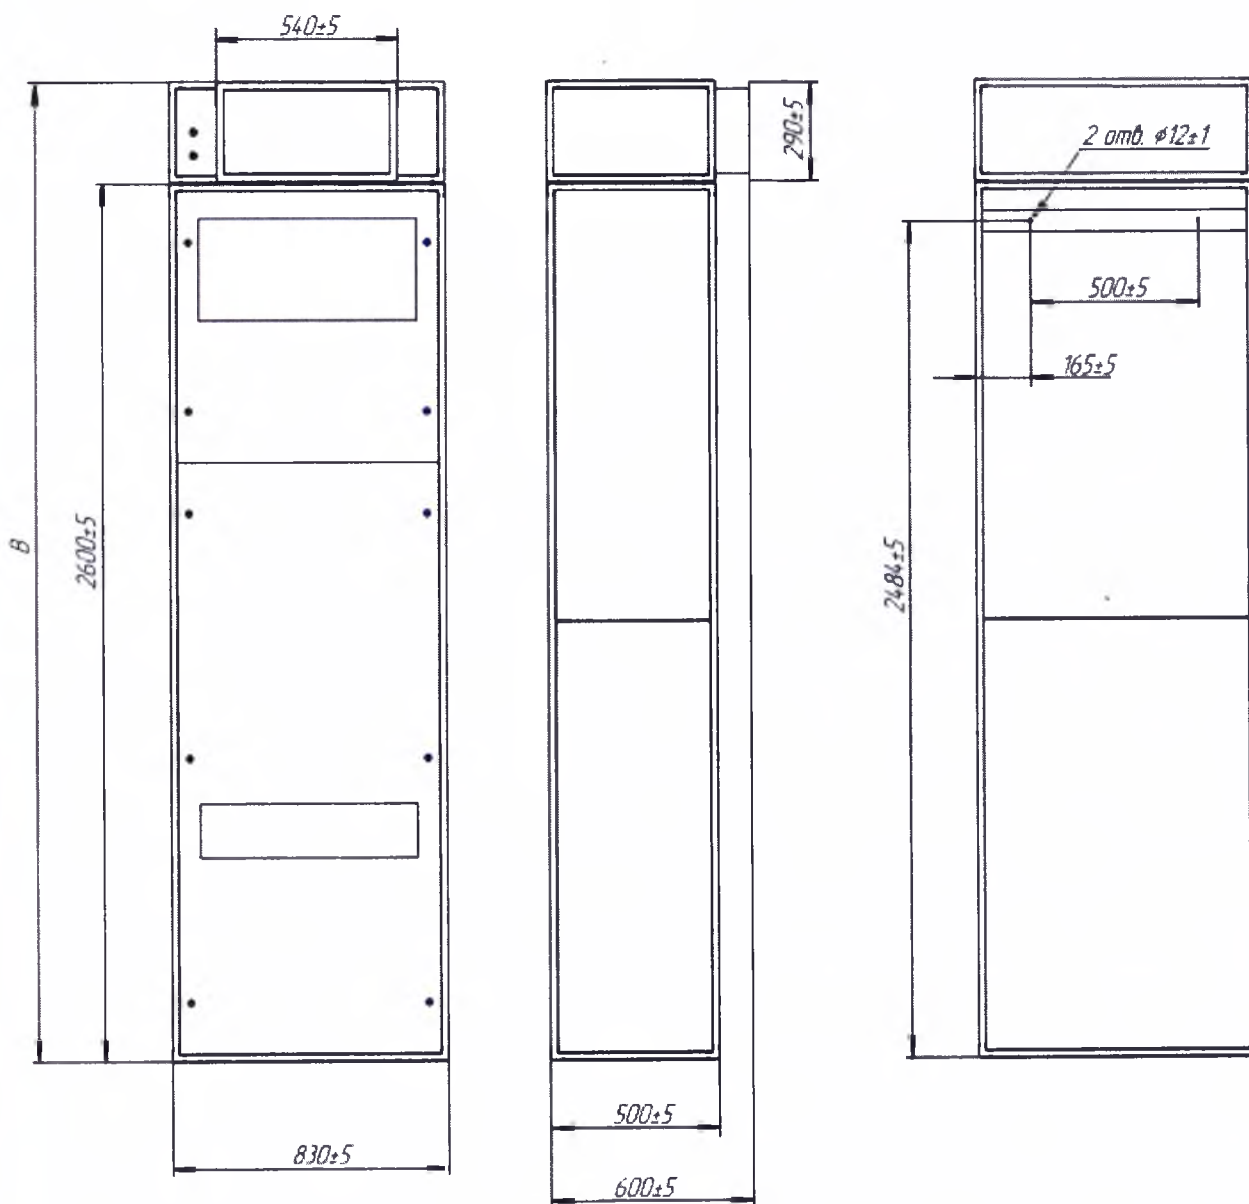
Габаритные и присоединительные размеры колонны рециркуляции
